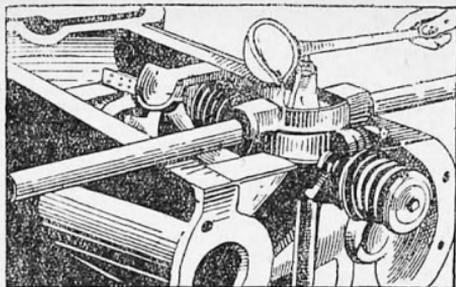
Заливка коренного подшипника с помощью специального прибора
